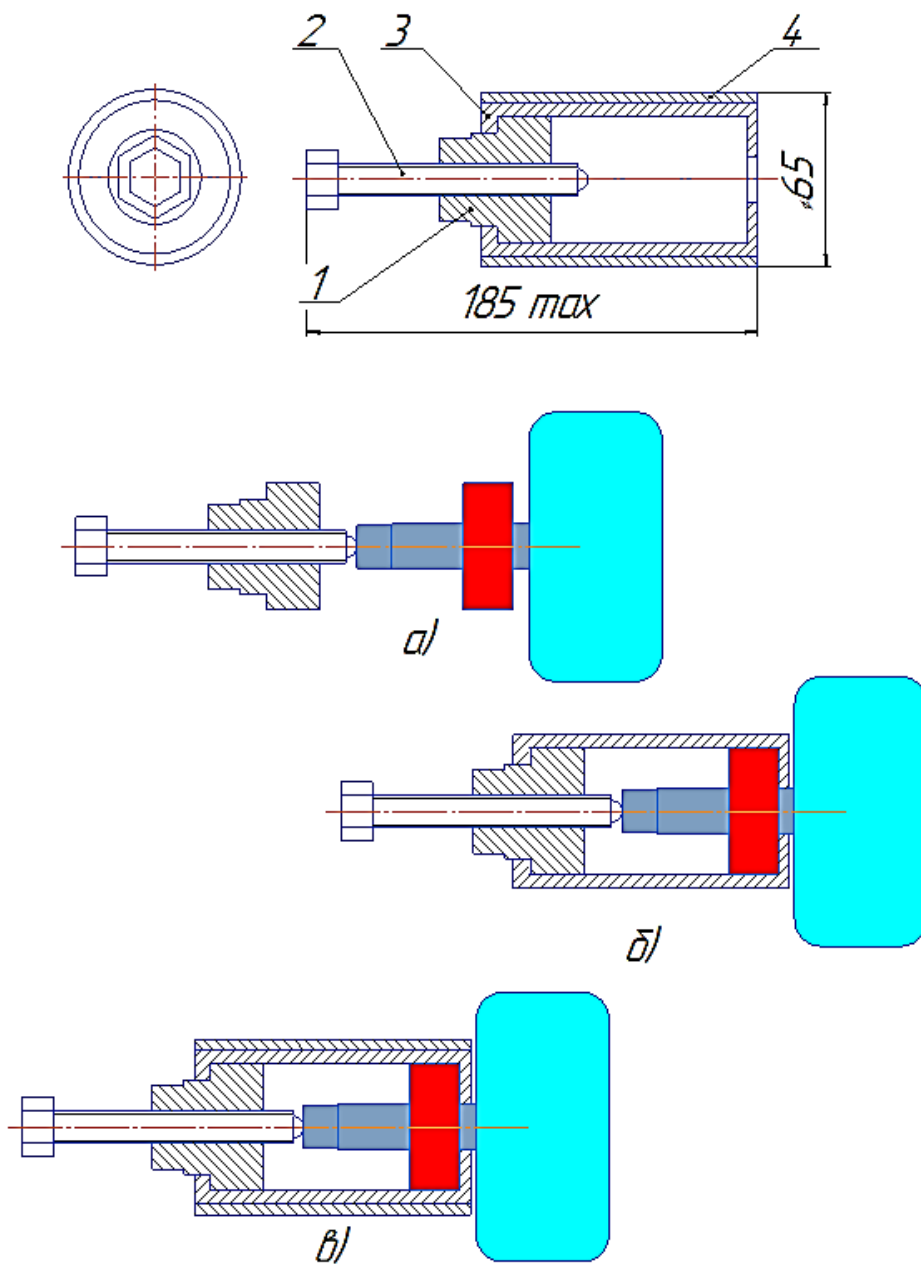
Принципова схема використання знімача підшипника з валу ротора
